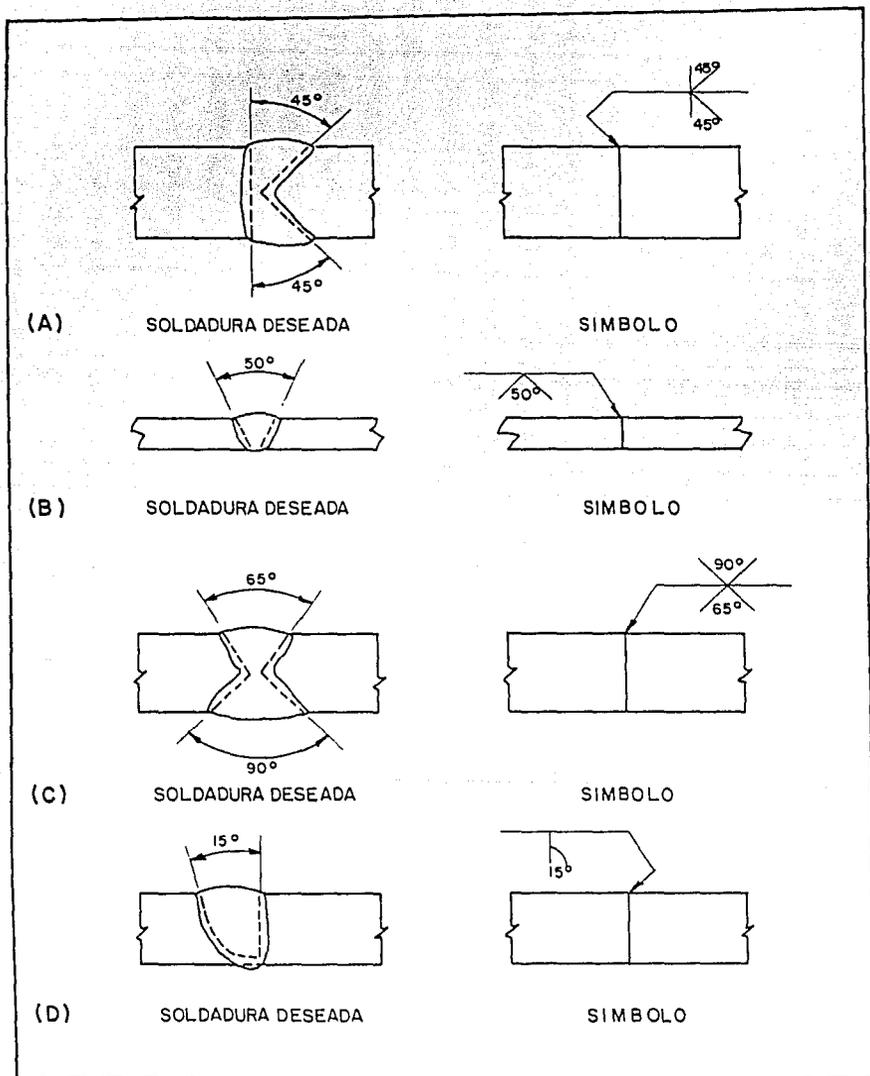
DESIGNACION DE ANGULO DE PREPARACION DE SOLDADURAS A TOPE
